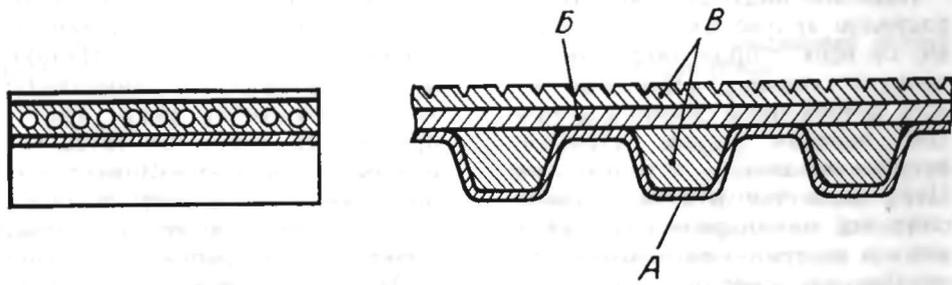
Конструкция специального зубчатого ремня для привода заднего колеса: А — нейлоновое покрытие; Б — полиуретановая основа; В — силовой волокнистый слой из кевлара
